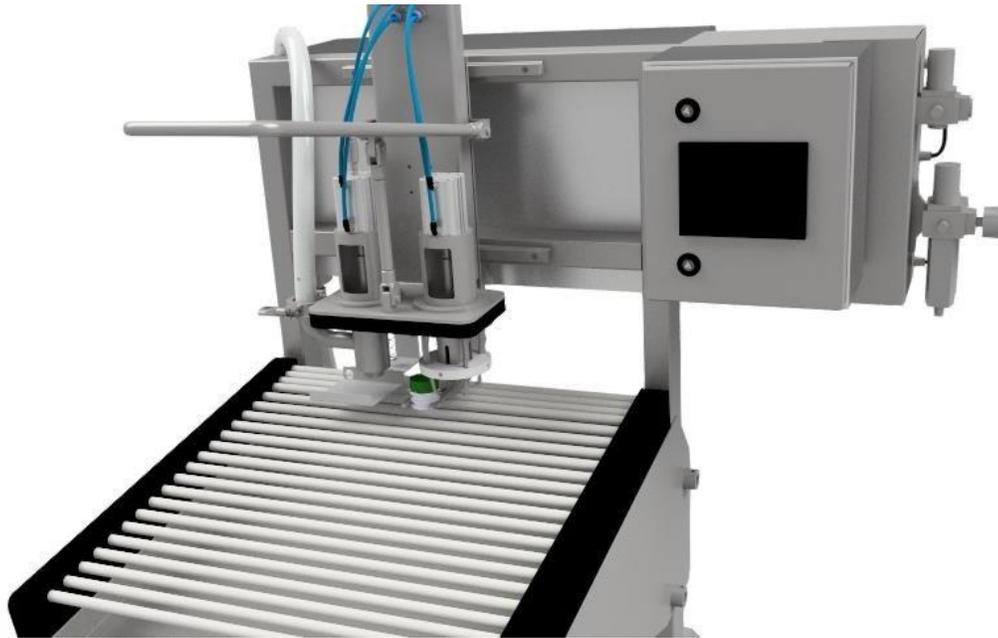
Plano de ensamble módulo de desplazamiento horizontal
